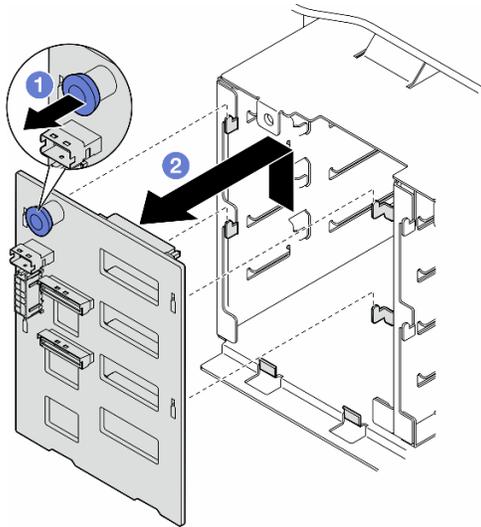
Entfernen einer Rückwandplatte für 3,5-Zoll-Laufwerke
